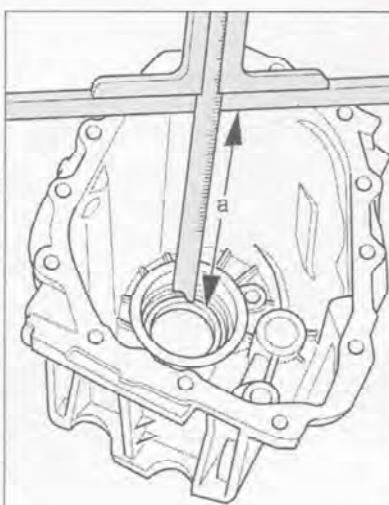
Измерьте расстояние a на новом и старом корпусе коробки передач.
